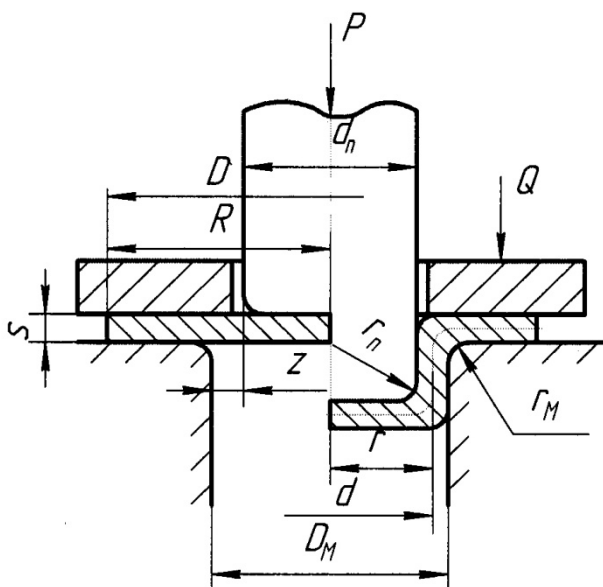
Схема процесса вытяжки стакана из плоской заготовки
